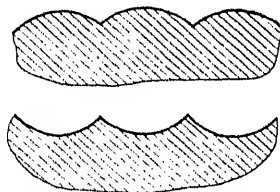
Два профиля поверхности с одинаковыми высотными параметрами
